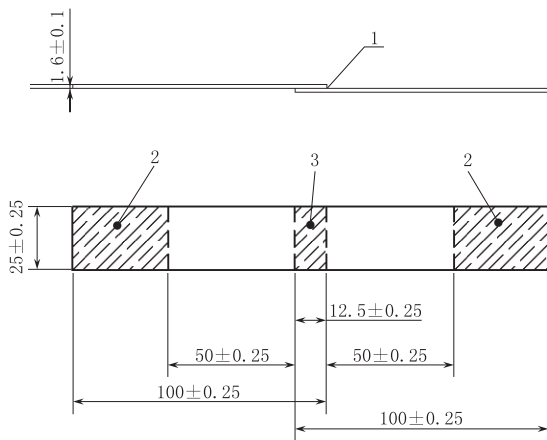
拉伸剪切试件的形状及尺寸 (单位: mm)
